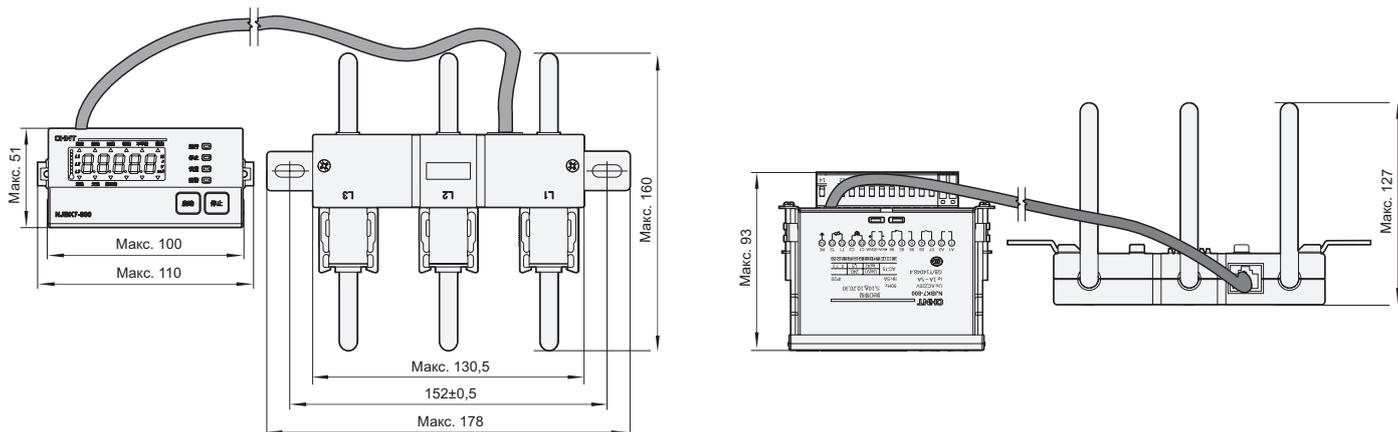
Габаритные и установочные размеры устройства защиты с номинальным током 400, 800 А
